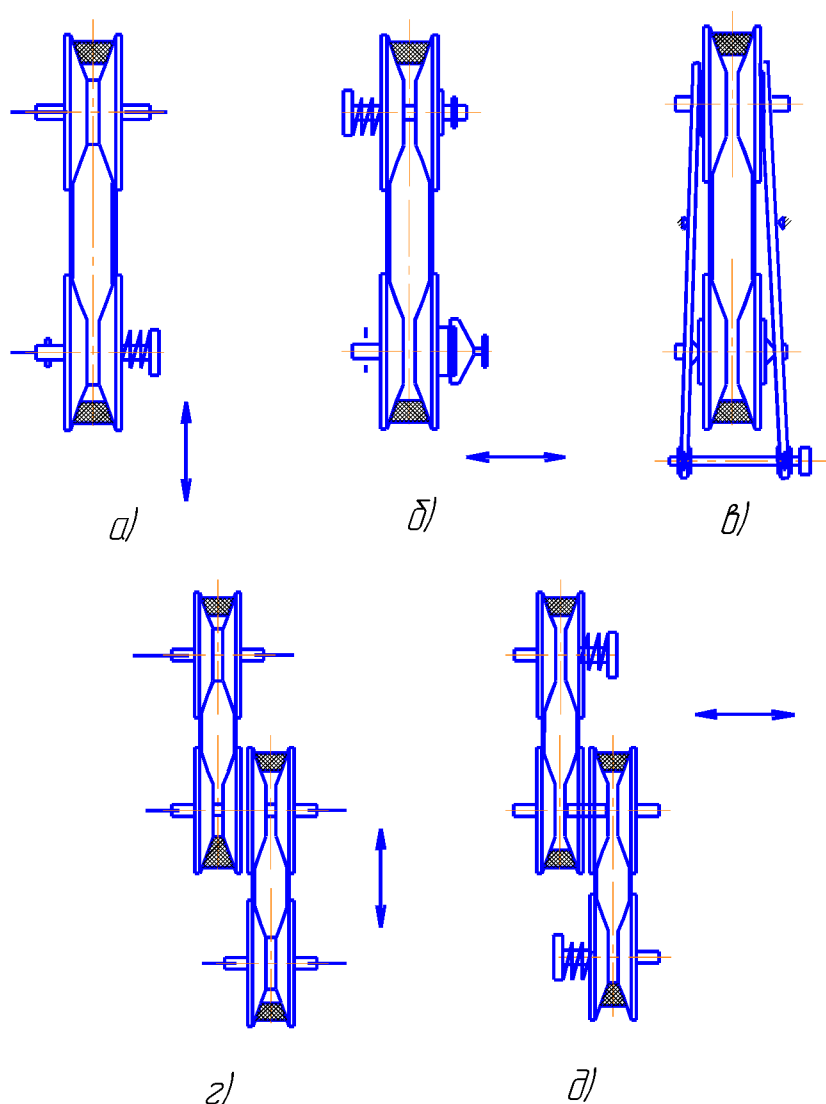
Схеми керування клинопасовими варіаторами
